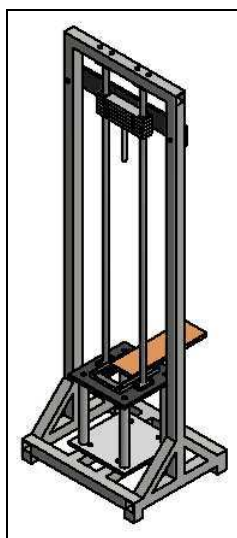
Esboço da concepção do subsistema elevação do conjunto massa/impactador.
